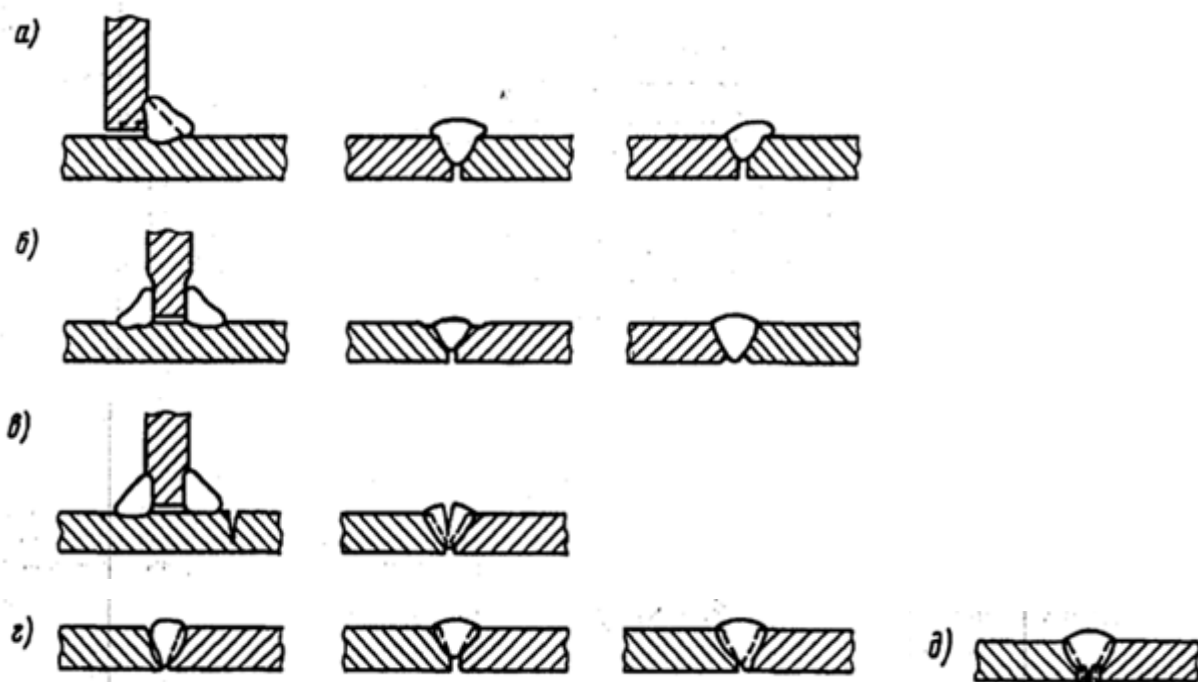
Наружные дефекты соединений: а - наплывы; б - подрезы; в - трещина в сварном шве и на основном металле; г - провары; д – прожог
